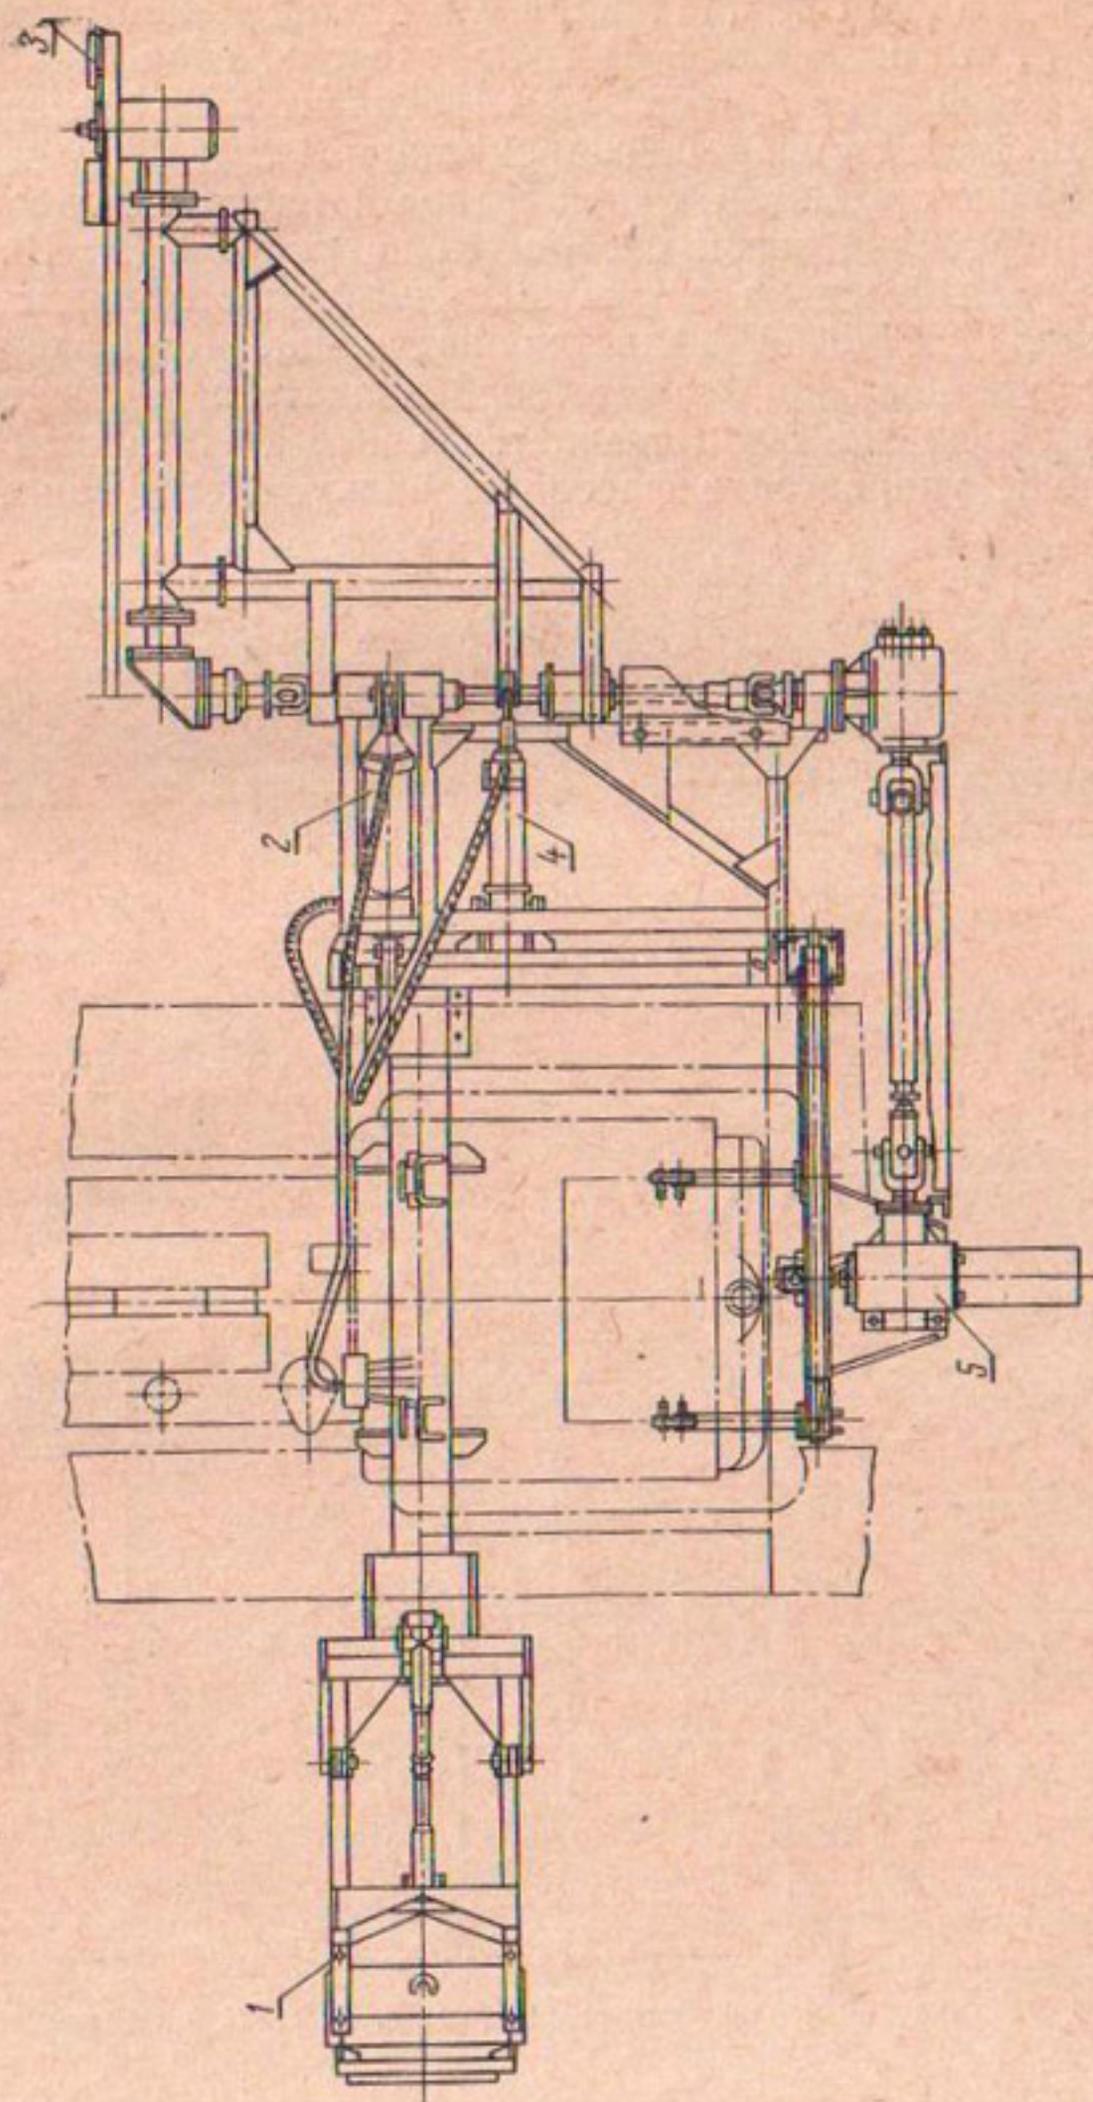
Конструкция навесного оборудования каналоочистителя Д-490М (фреза):
